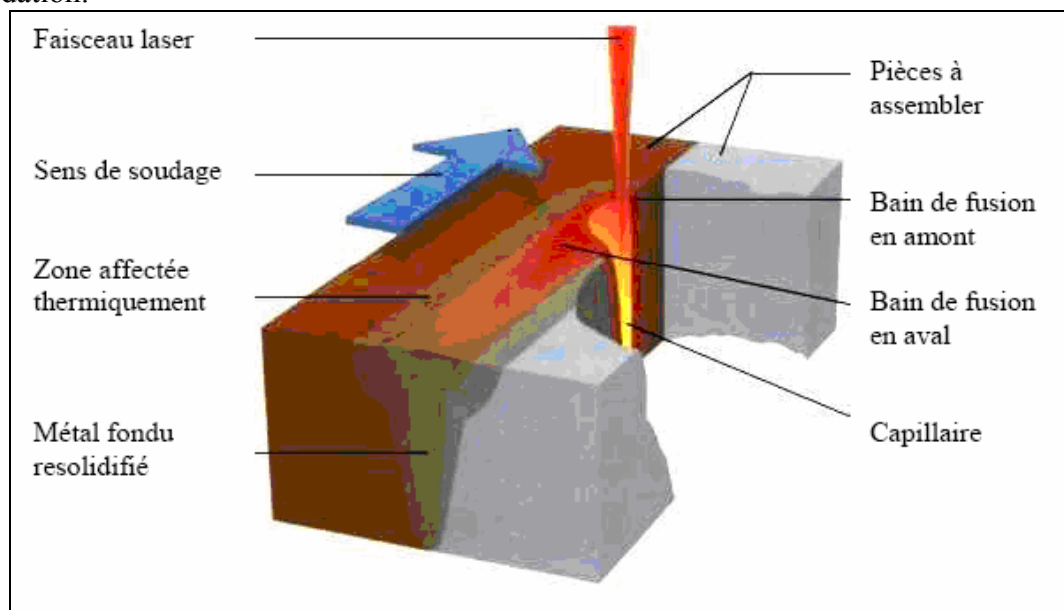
Principe de soudage par faisceau laser [2]
